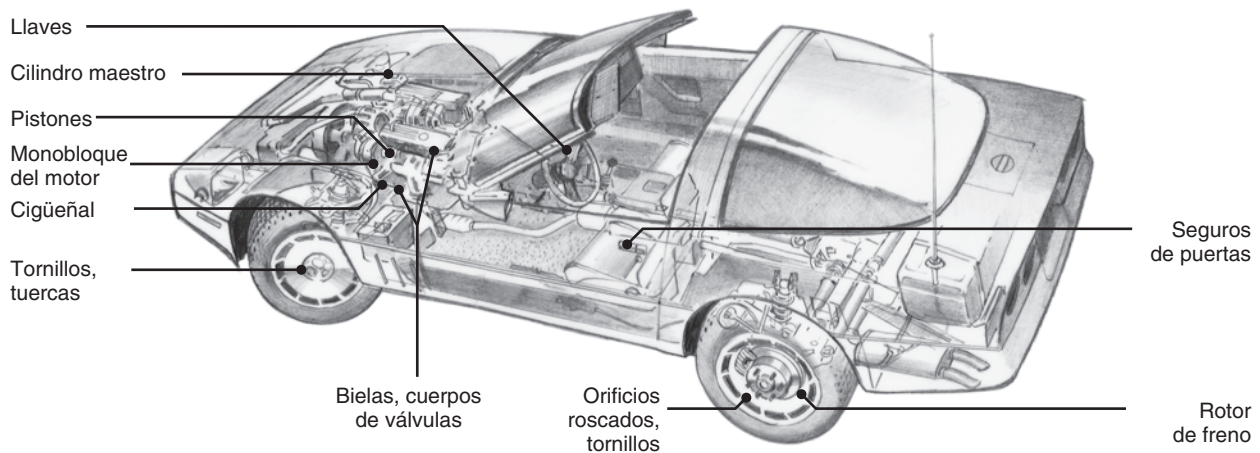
Partes comunes de un automóvil que requieren operaciones de maquinado para adquirir las características superficiales, dimensiones y tolerancias deseadas.
